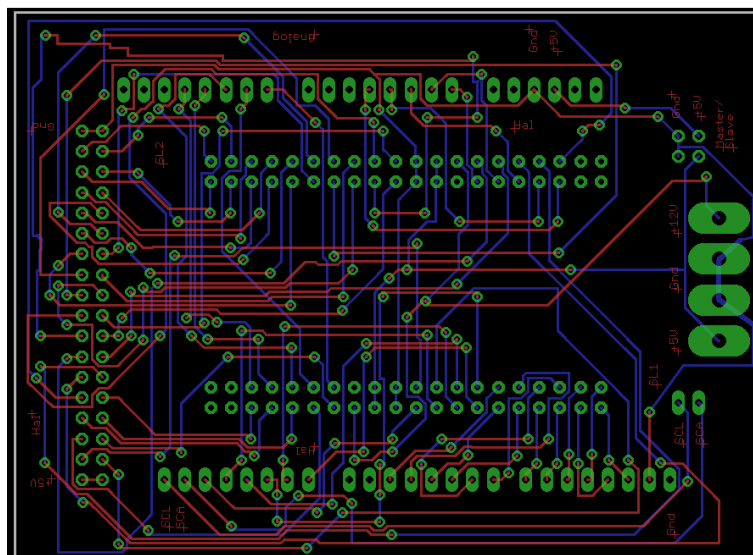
Layout des Shields. Rot: Top-Layer; Blau: Bottom-Layer.
